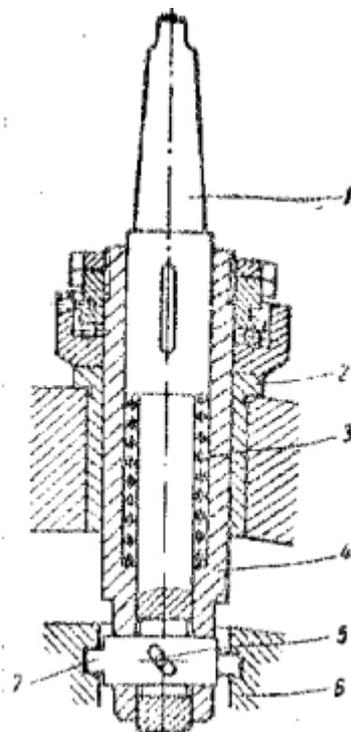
Приспособление для растачивания кольцевых канавок на сверлильном станке.
